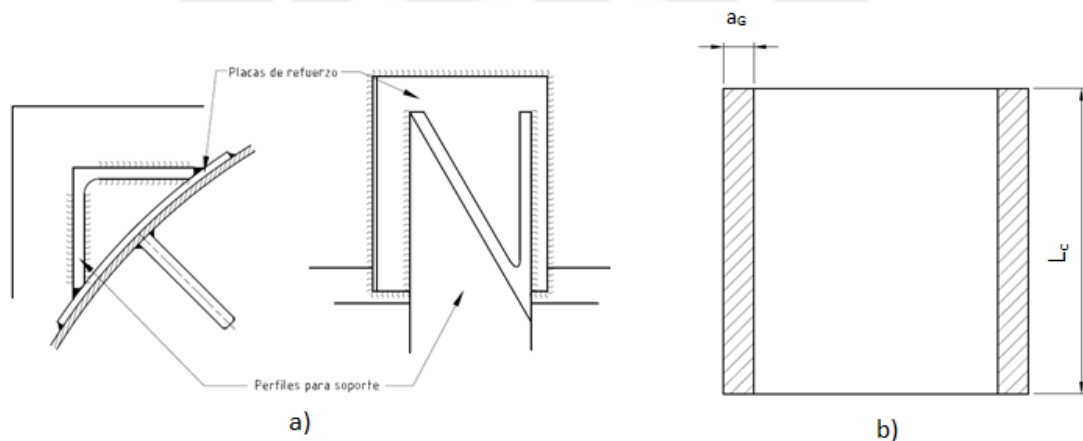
a) unión de las patas al recipiente; b) área proyectada de la unión soldada entre las patas y las placas de refuerzo
